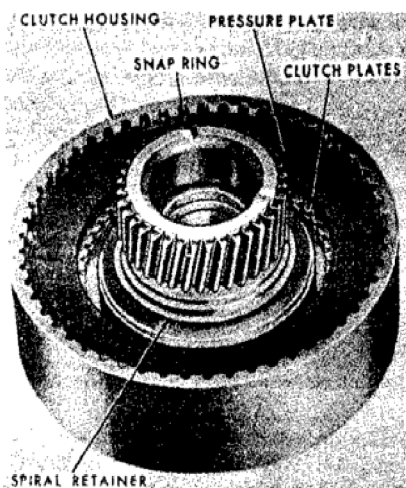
Direct drive koppeling en "A" zonnegas, montage.
